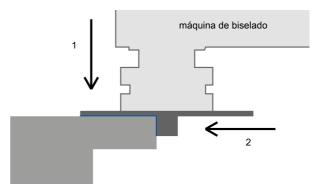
Adjuntar la herramienta de desbarbado borde KE 10 a la pieza de trabajo
